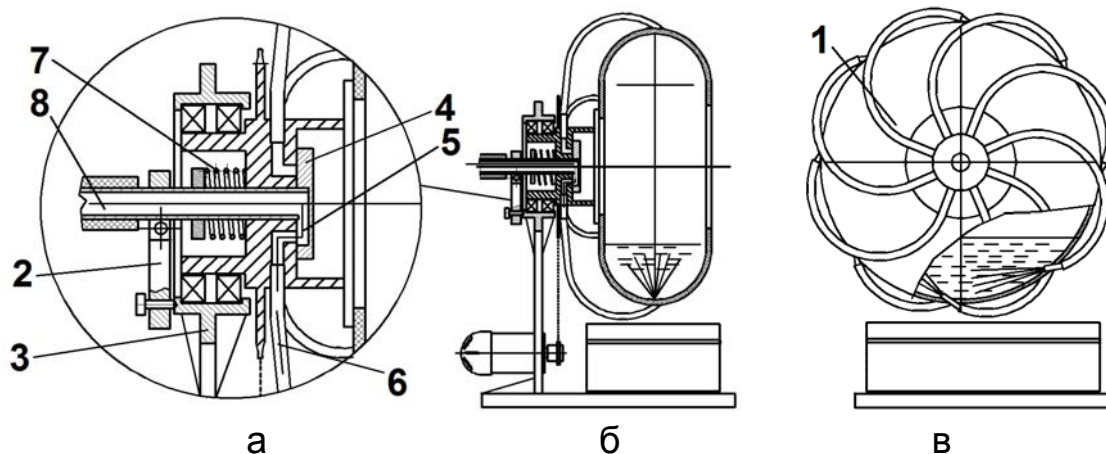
Струйно-абразивная установка с горизонтальной осью вращения рабочей камеры: а – золотниковое устройство, обеспечивающее подачу сжатого воздуха к затопленным соплам; б – рабочая камера в разрезе; в – вид слева (стойка с золотниковым устройством условно не показаны)
